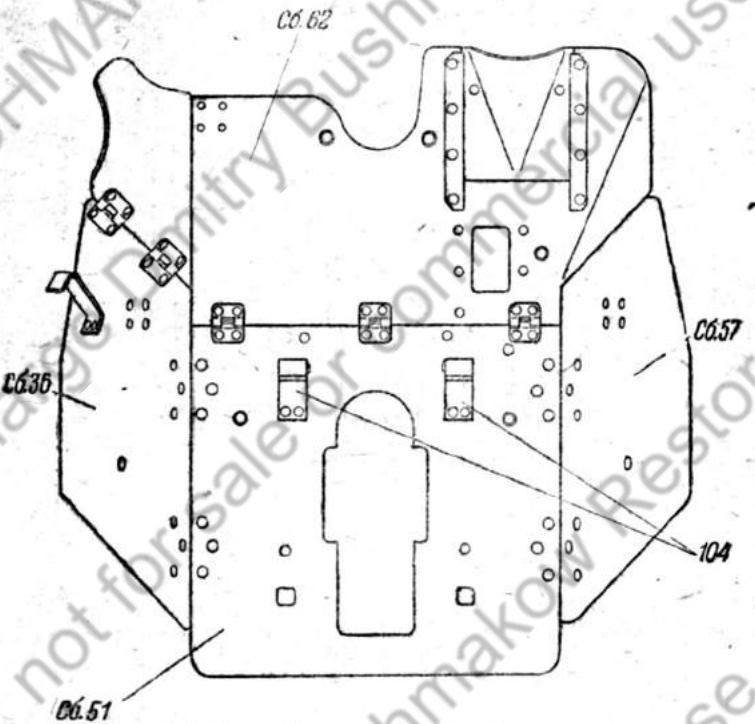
Верхний щит (Сб. 04). Вид спереди:
